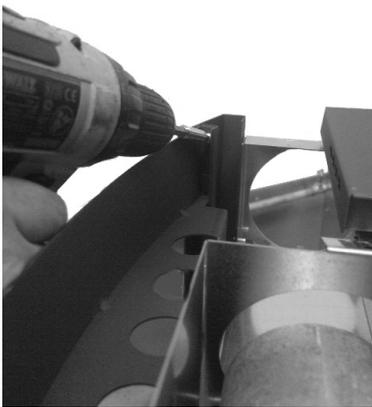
Die Schrauben auf der Rückseite entfernen
